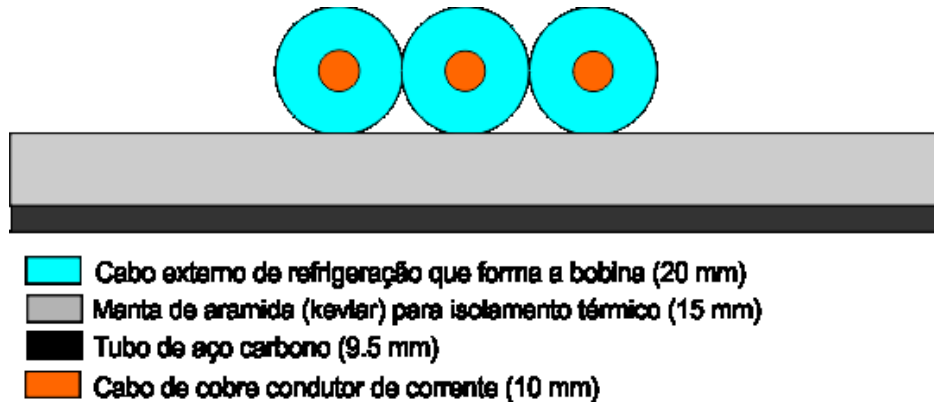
Esquemático da montagem da bobina de aquecimento por indução e do isolamento de aramida sobre a parede externa do tubo, com dimensões de cada componente.
